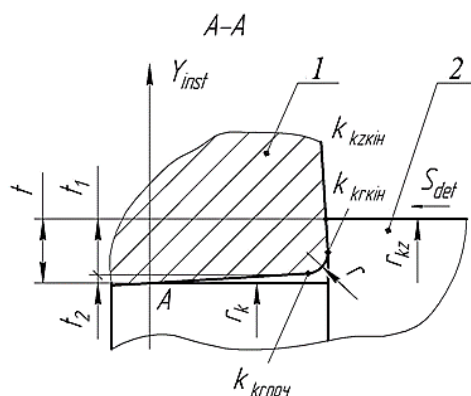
Розріз А-А зуба фрези при обробці кулачка розподільного вала зі схрещеними осями інструмента та деталі: 1 – фреза; 2 – розподільний вал
